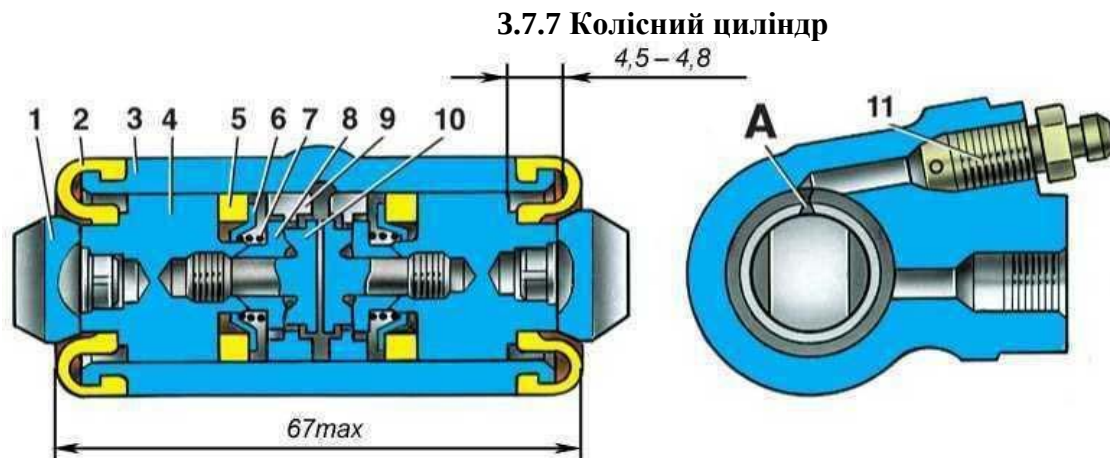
Задній колісний гальмівний циліндр автомобіля ВАЗ: 1 - упор гальмівної колодки; 2 - захисний ковпачок; 3 - корпус гальмівного циліндра; 4 - поршень; 5 - ущільнювач; 6 - опорна тарілка; 7 - пружина; 8 - сухарі; 9 - упорна манжета; 10 - упорний гвинт; 11 - штуцер; А - проріз на упорній манжеті.
